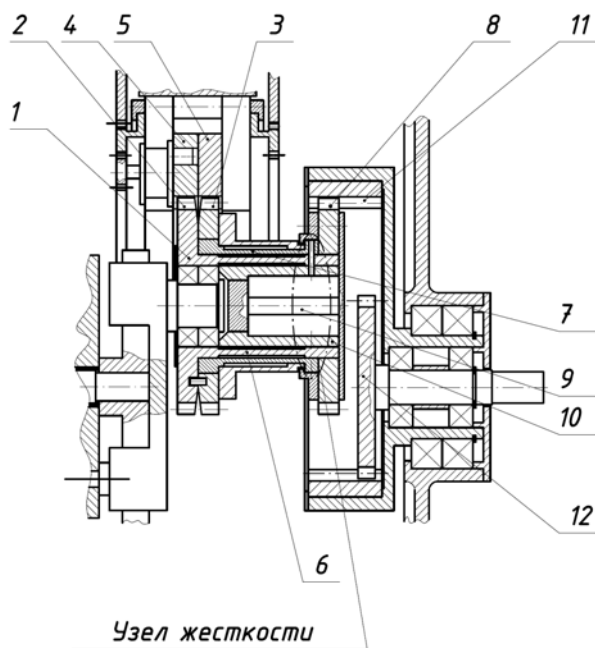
Конструкция компенсатора погрешности угла поворота сателлита
